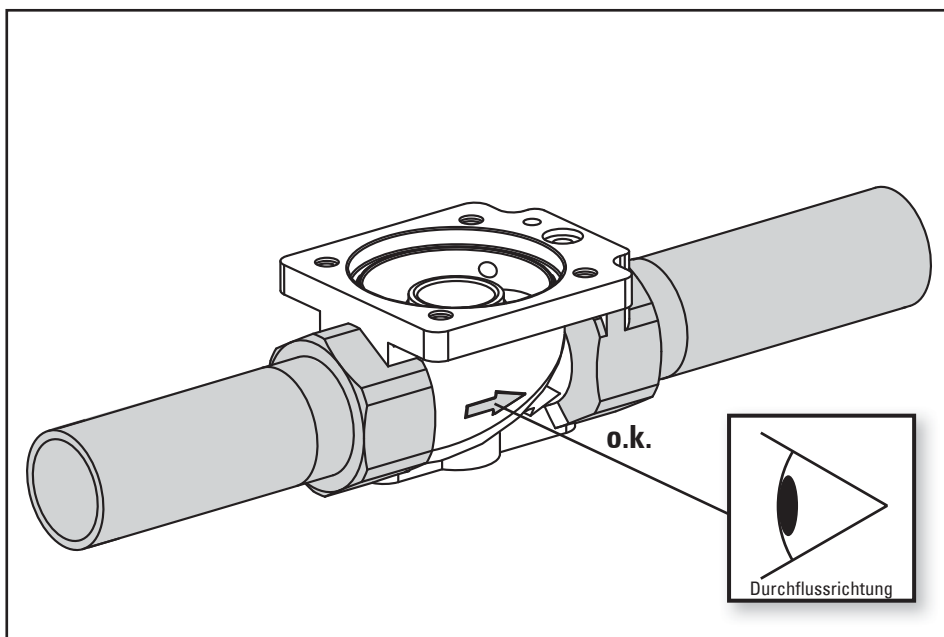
Einbau: Anschweißen, Einschweißen des Magnetventilgehäuses
